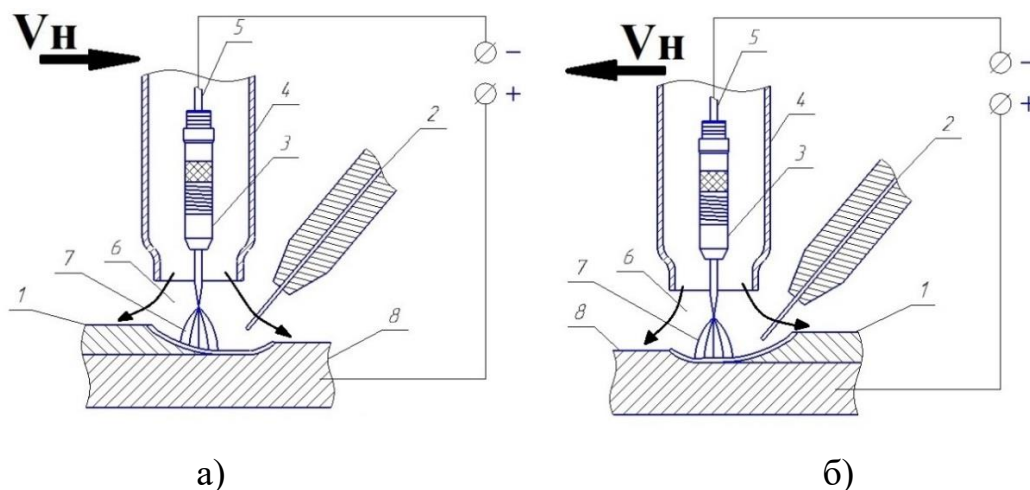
Схема процесса аргонодуговой наплавки неплавящимся электродом: а) левый способ наплавки (проволока подается в головную часть сварочной ванны) б) правый способ наплавки (проволока подается в хвостовую часть сварочной ванны),
